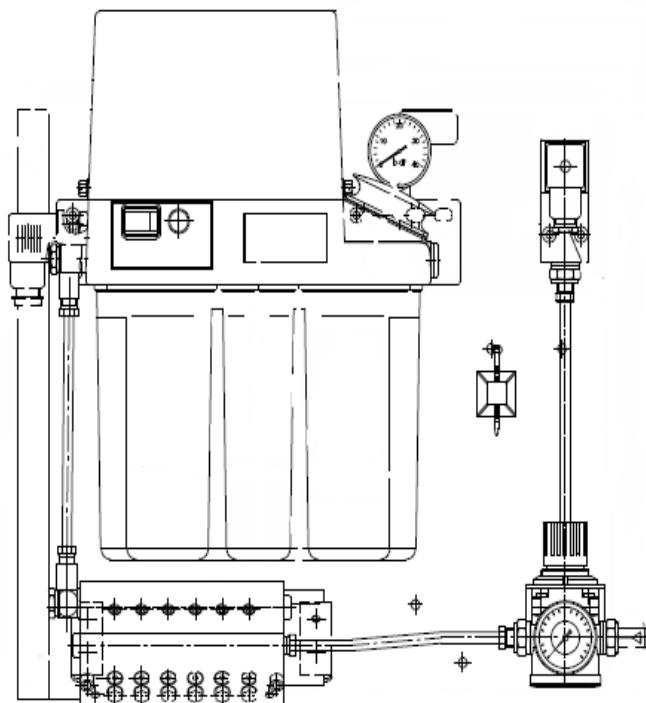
Baugruppe für das Luft-/Öl-Schmiersystem für Motorspindel
